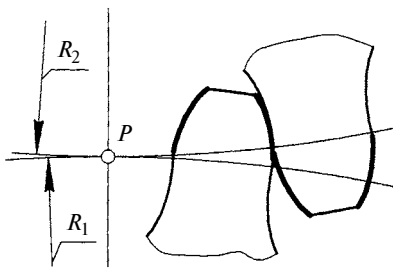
Зубчатая передача с оптимальными профилями зубьев
